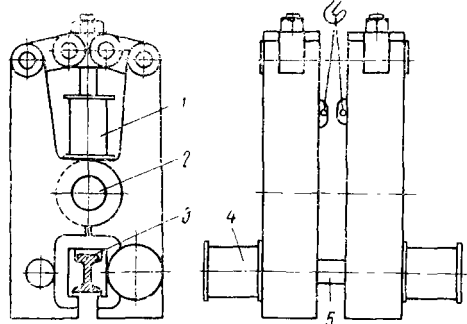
Схема подвесной стыковой машины для сварки рельсов с контурным трансформатором
